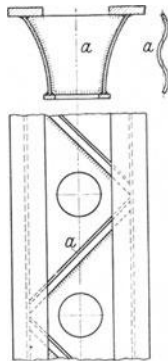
Geschweißtes Drehbankbett (Diagonalverstrebung).
